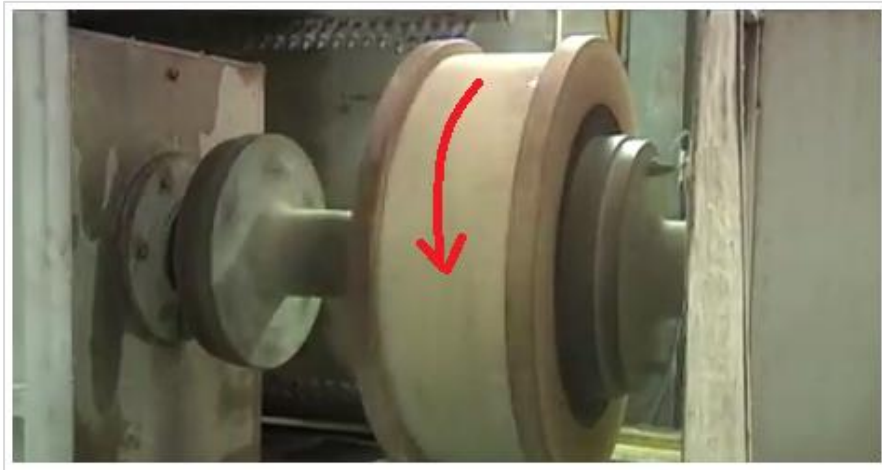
Dispositivo de suporte com rotação (DSE Bearing Co.,Ltd 2011).
